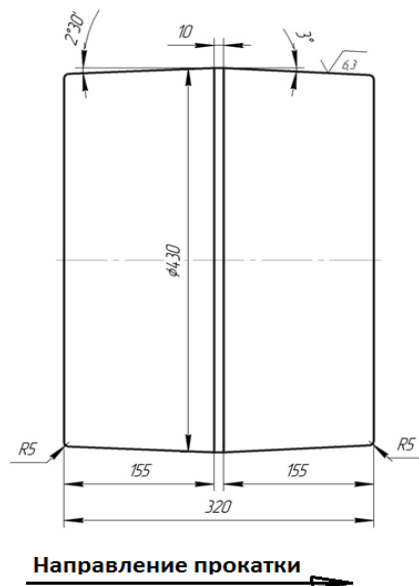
Бочка валка прошивного стана МИСиС-130Д
